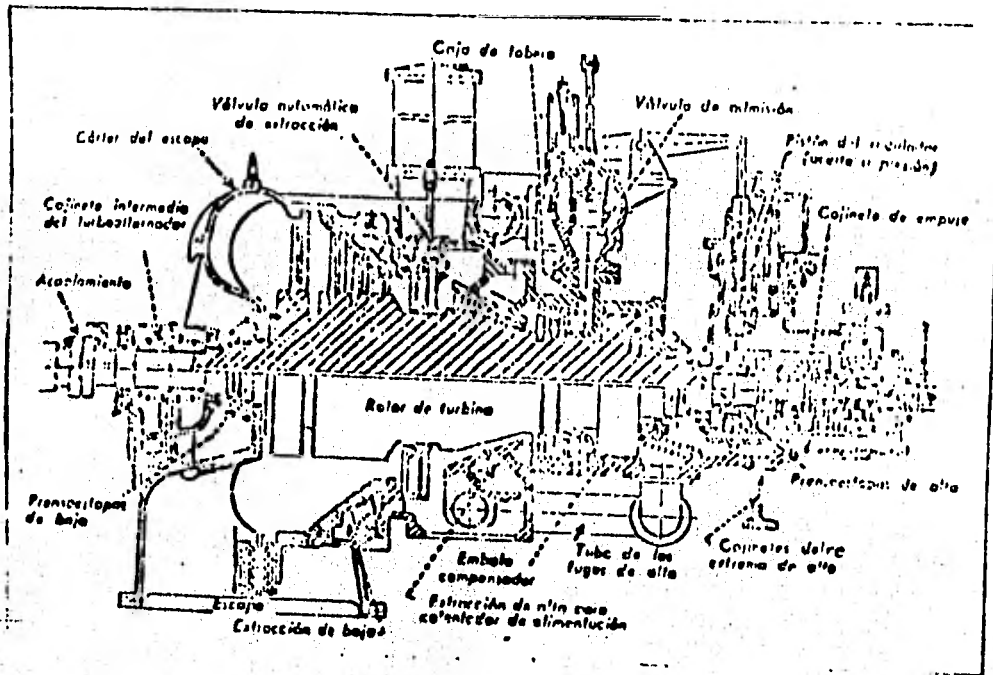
, Corte longitudinal de una turbina (con extracción de vapor) de 10 000 Kw, 3600 r.p.m.
